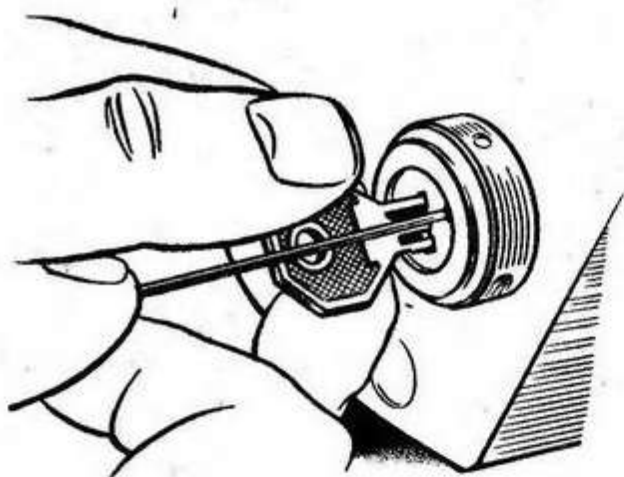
Нажатие на стопорную пружину для извлечения запорного цилиндра выключателя зажигания
